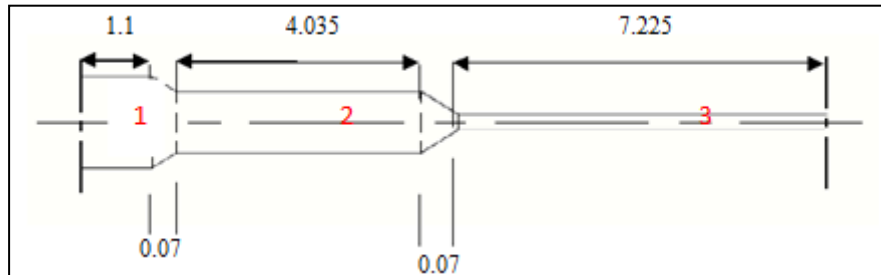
Différentes sections composant la poutre en béton précontraint.
